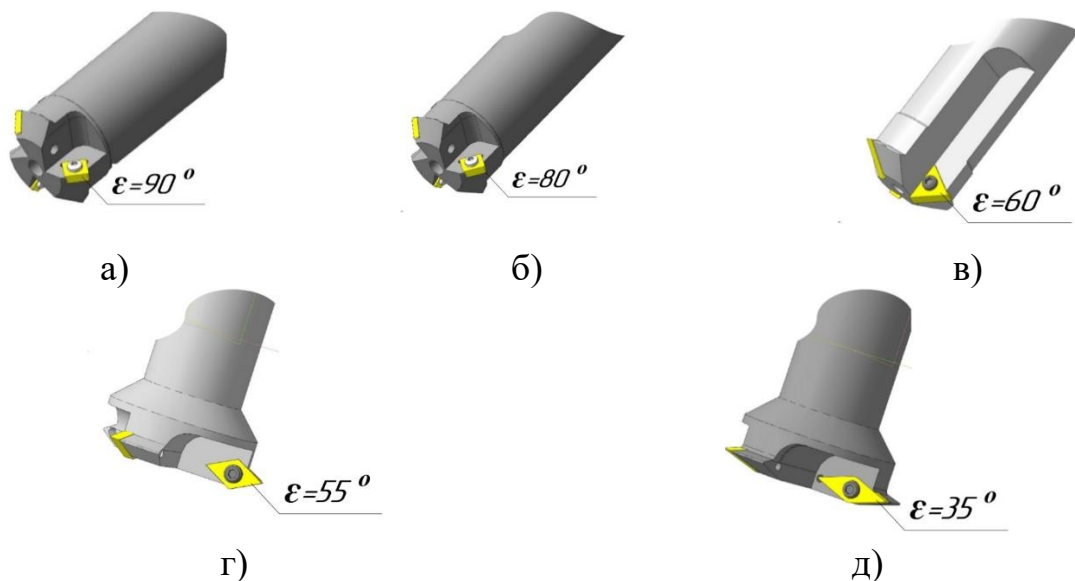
Різальні пластини для токарної обробки типу: а) SCMT; б) CCMT; в) TCMT; г) DCMT; д) VCMТ
